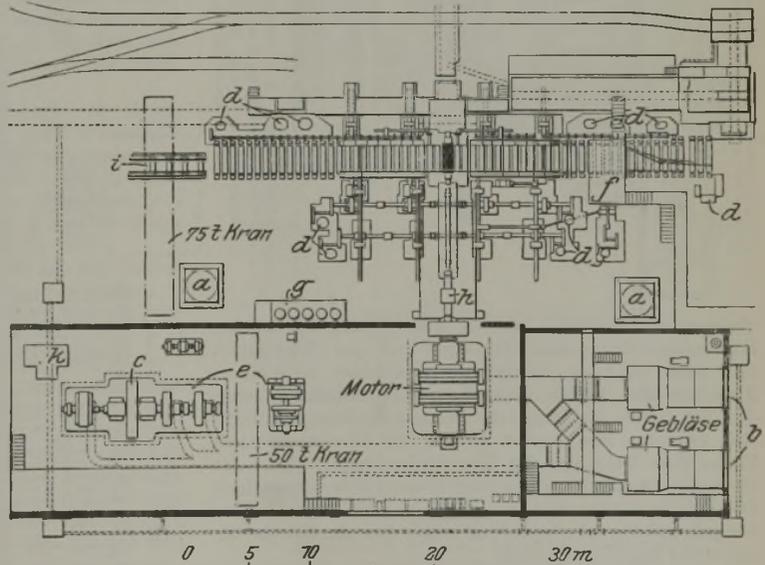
Lageplan der 1016-mm-Blockwalze.
